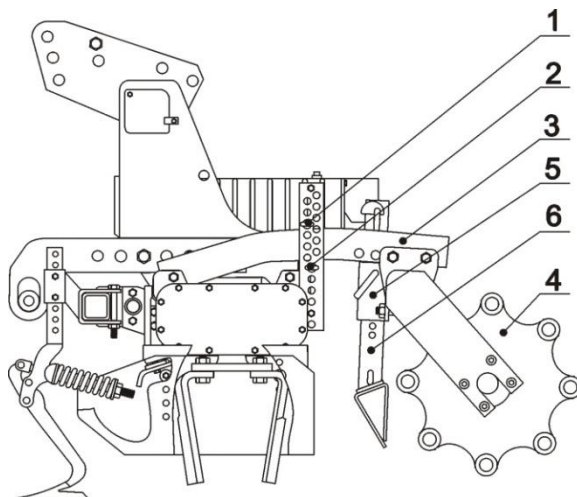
Регулировки глубины обработки и планировочного бруса:
